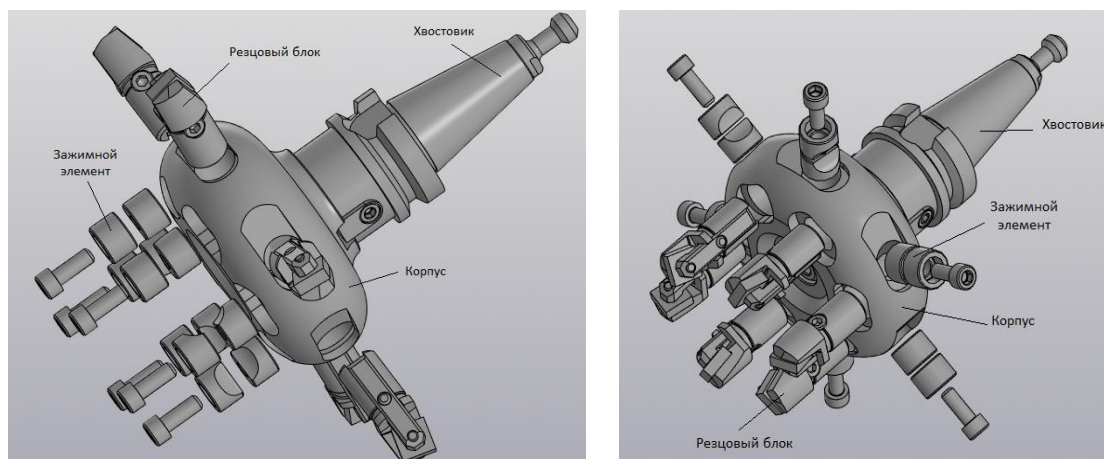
Конструктивная схема и 3D модель дисковой фрезы
